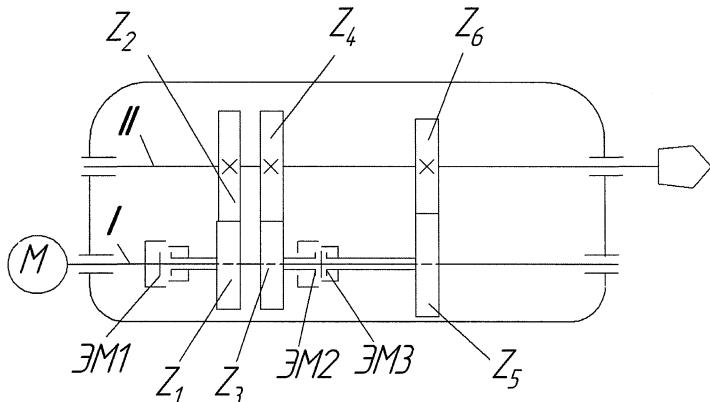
Двухваловая коробка скоростей со сцепными муфтами
